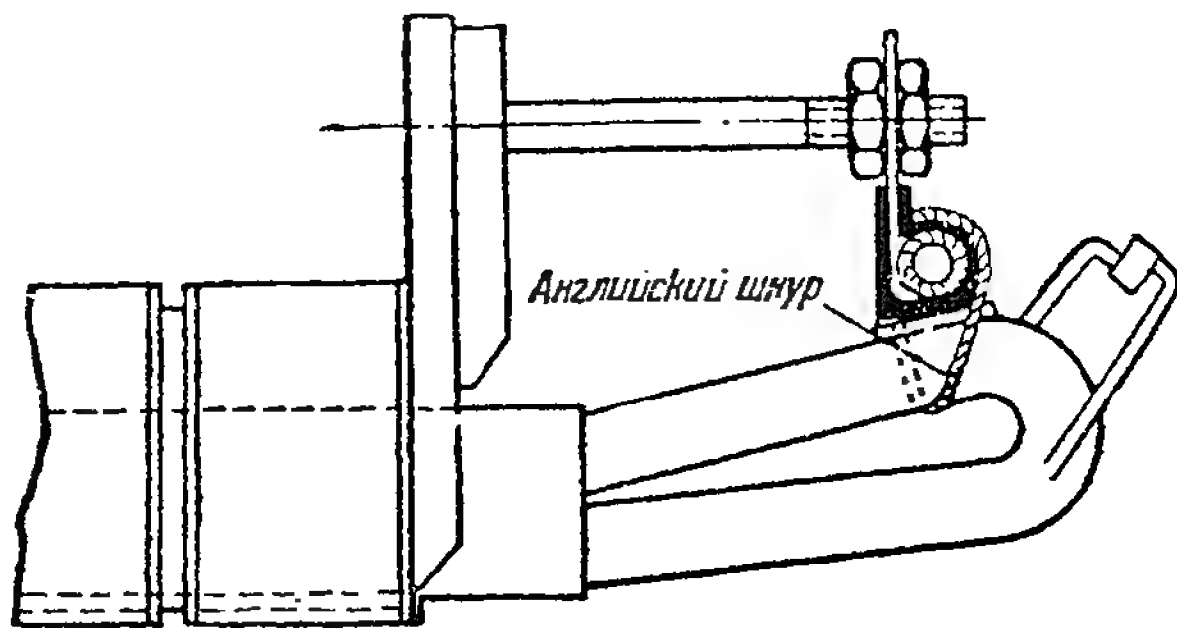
Крепление лобовых частей двухслойной обмотки.
